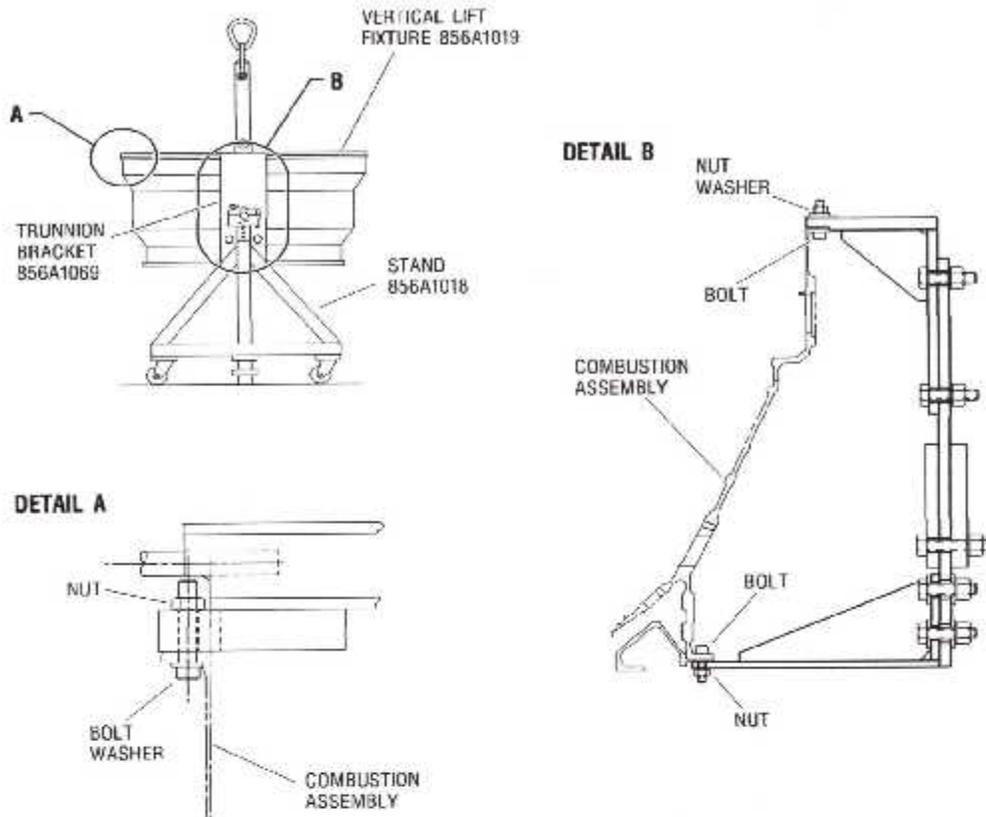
Installation de l'Ensemble de Combustion sur le Support, 856A1018G04.
